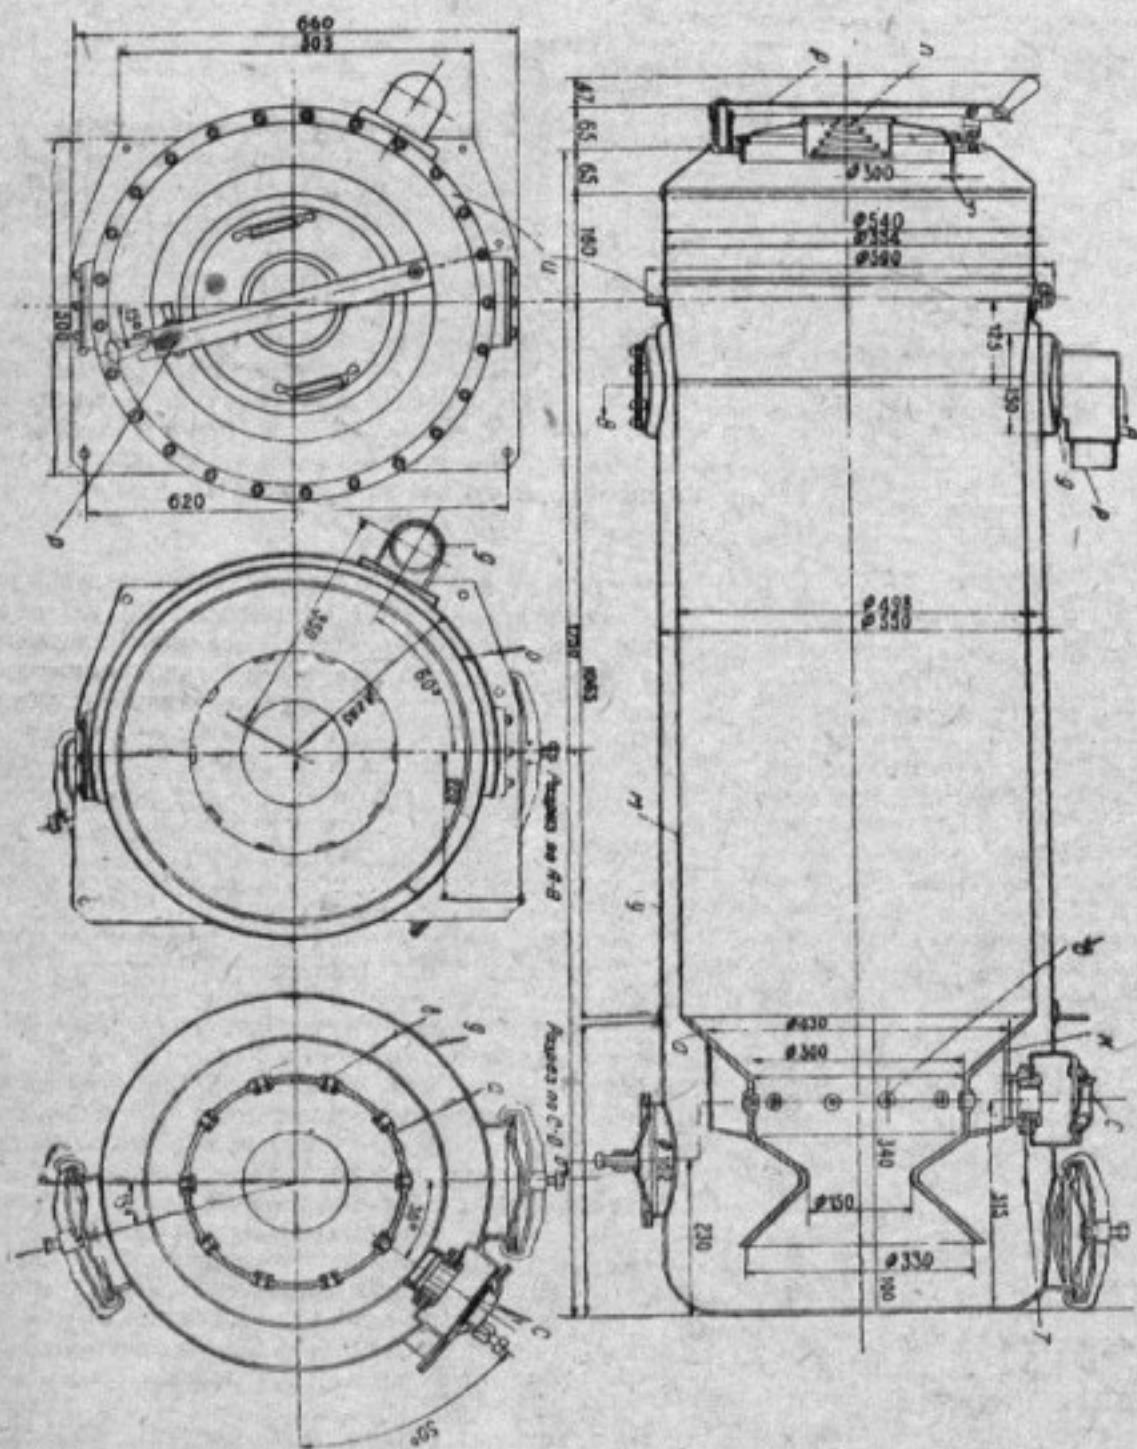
Газогенератор, установленный на машине ЗИС: м—внутренний кожух, у—наружный кожух, а—топливник, в—сопла, к—воздушная коробка, п—пружина, р—прижимная планка, д—патрубок отбора газа, с—возвратный клапан
